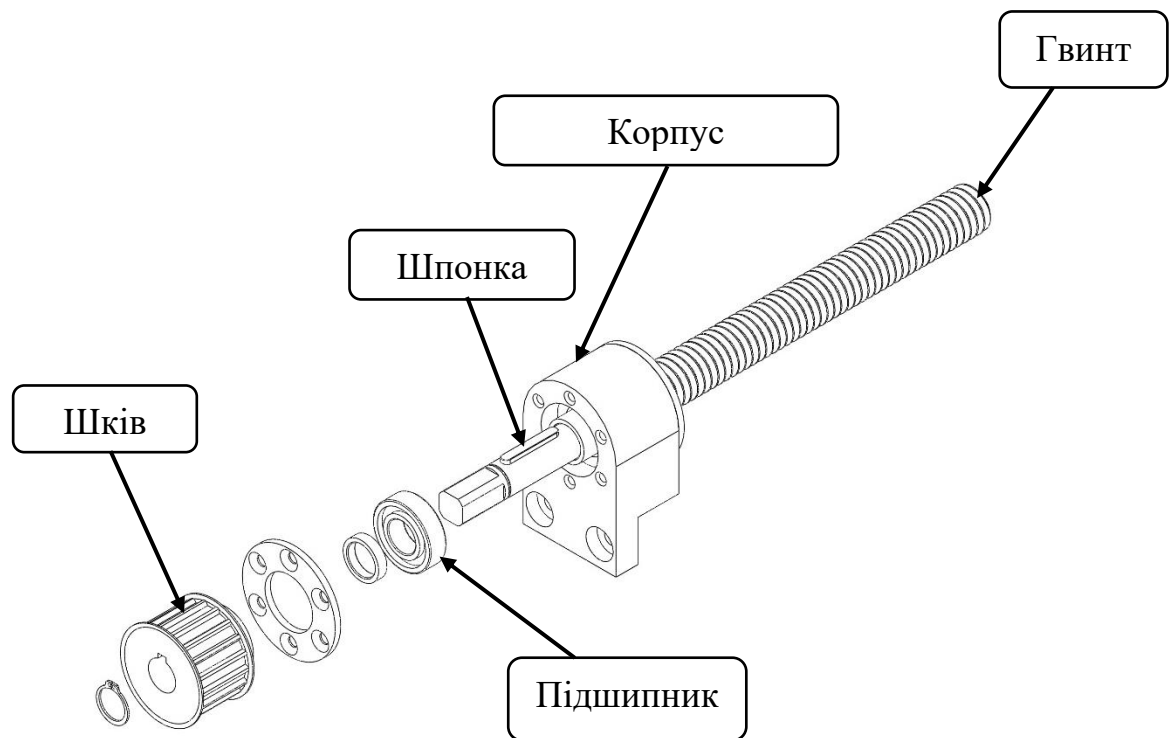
Привідний гвинт механізму регулювання ширини та елементи приводу
